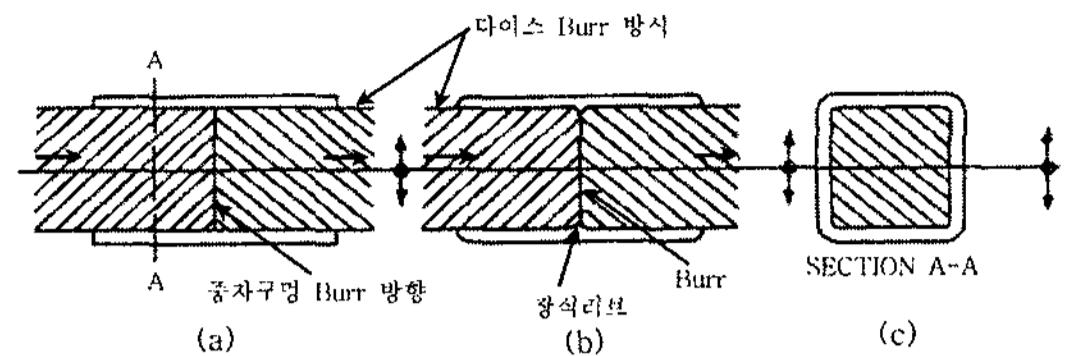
중자의 접층면의 Burr 발생과 대책
